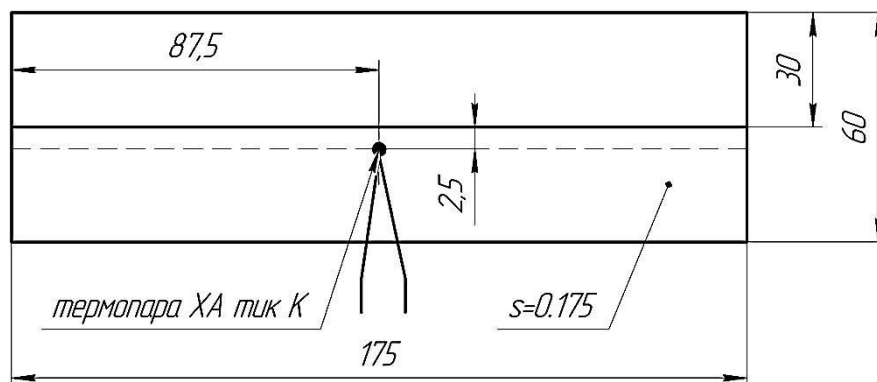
Геометричні розміри пластин під експериментальне зварювання та схема приварювання термопари
